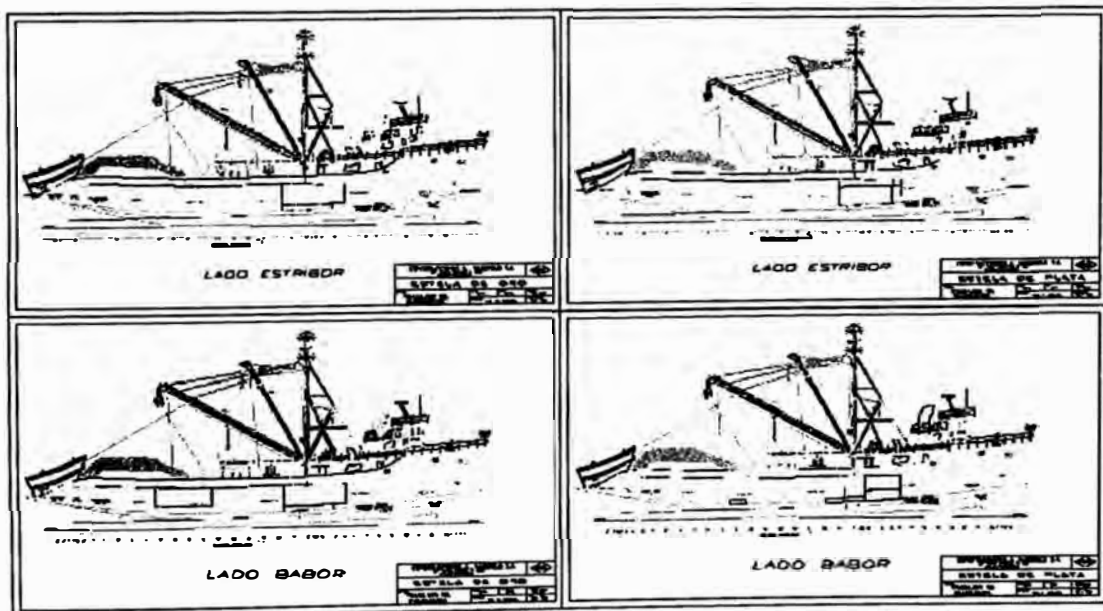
Vistas de los sectores del casco por cambio de planchas no previsto.
